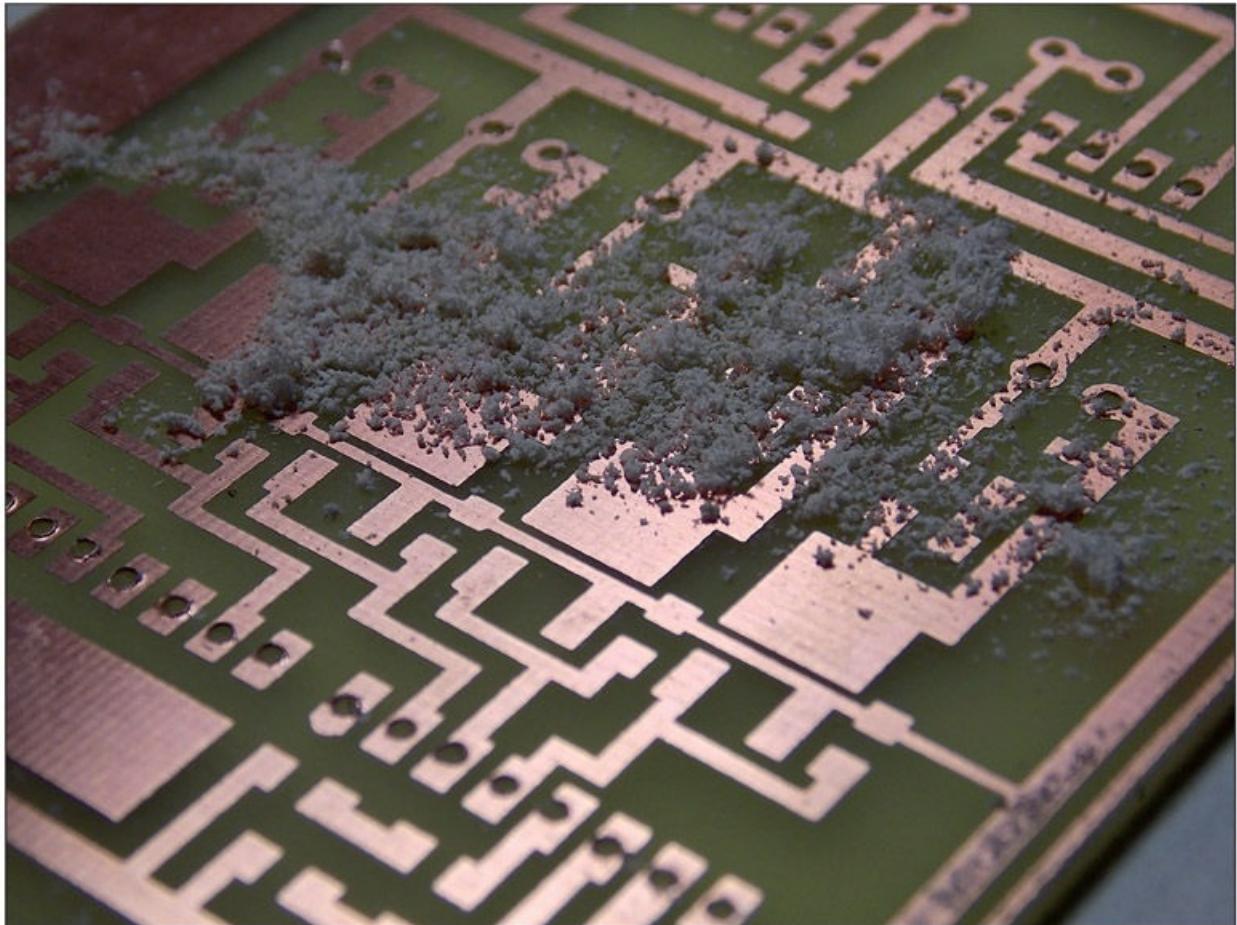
El circuito impreso perforado está listo para la soldadura de los elementos.
